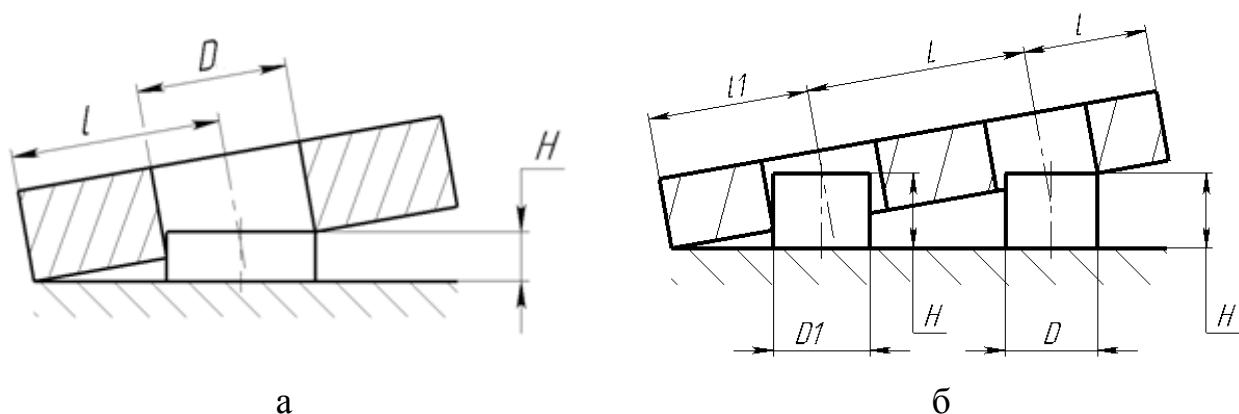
Схема установки заготовки (а – на один палець; б – на два пальці)
